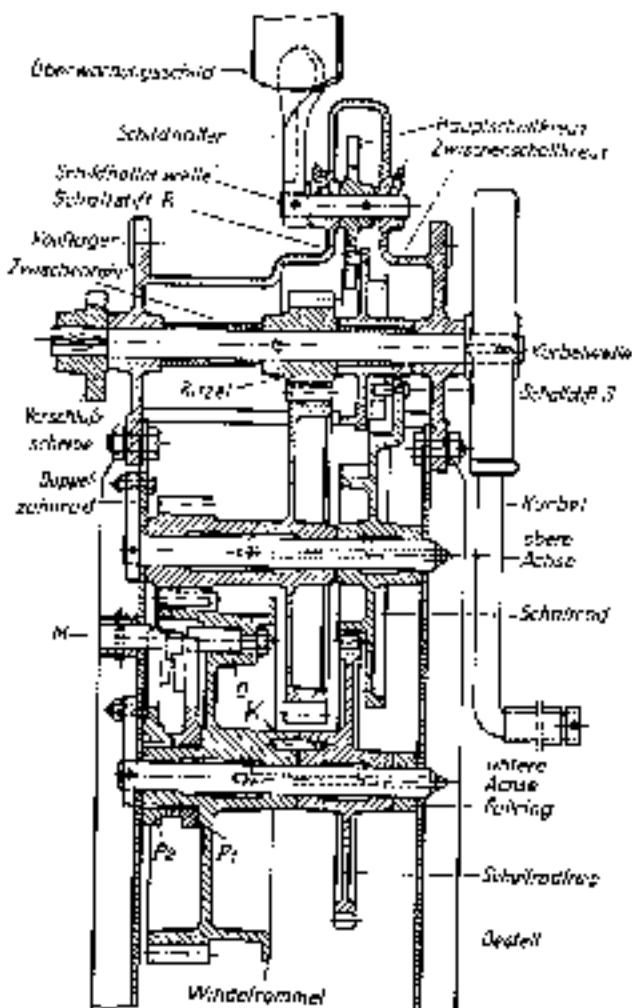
Schnitt durch die Winde für zuläufige Schranken
